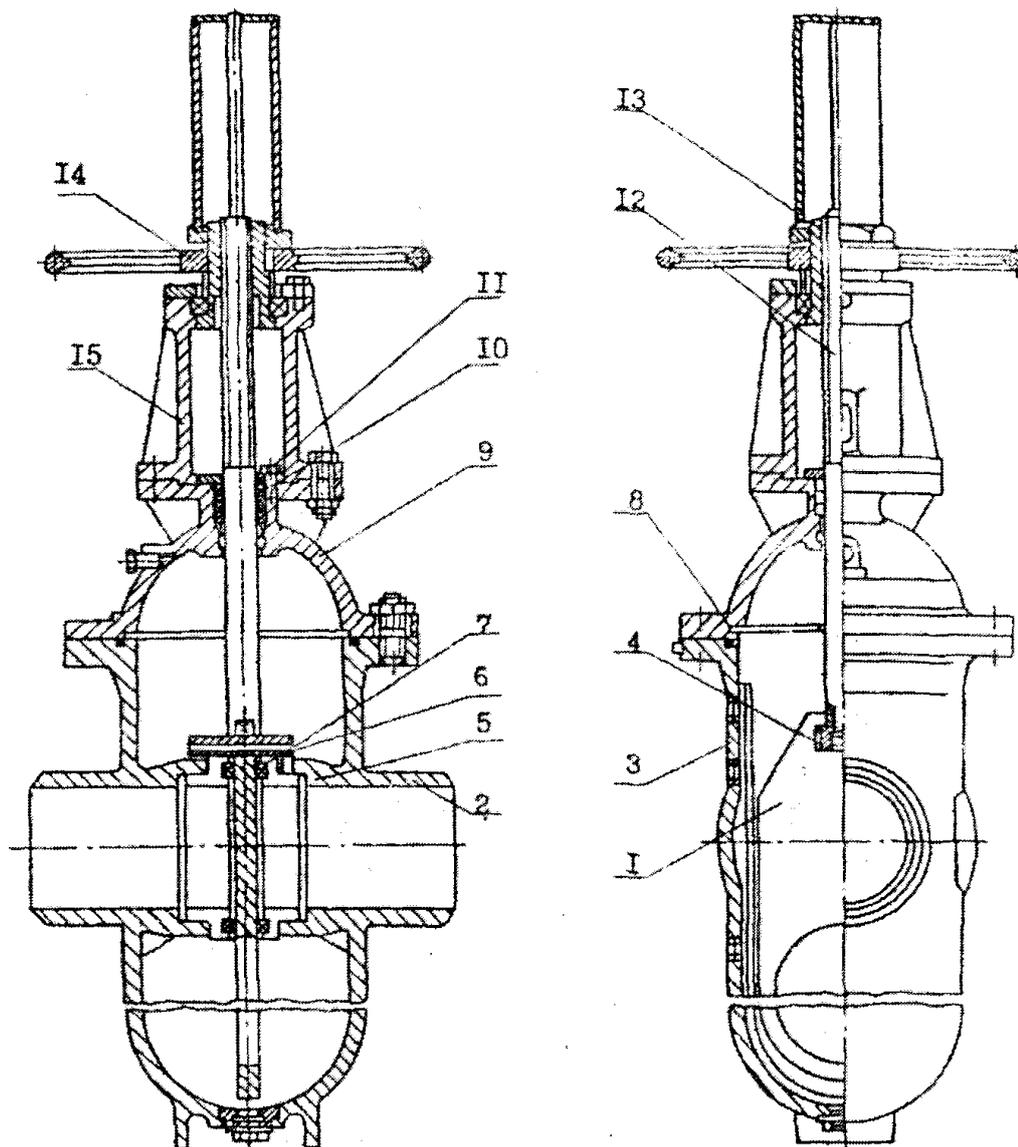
Параллельная однодисковая задвижка: 1 - шибер; 2 - патрубок; 3 - корпус; 4 - узел крепления шпинделя и шибера; 5 - седло; 6 - шпилька; 7 - уплотнительное кольцо; 8 - прокладка; 9 - верхняя крышка; 10 - набивка сальника; 11 - нажимная планка; 12 - шпиндель; 13 - кожух; 14 - элемент привода; 15 - стойка.
